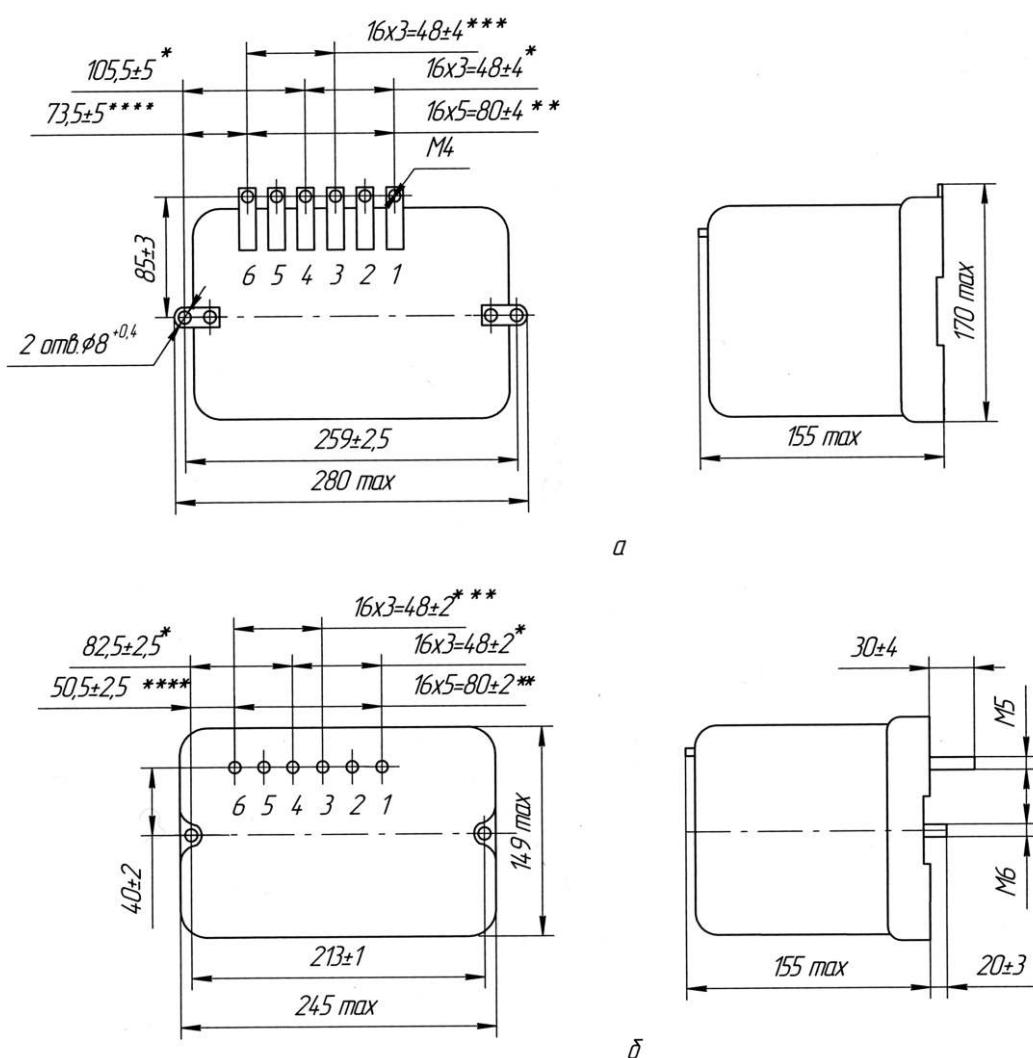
Габаритные, установочные, присоединительные размеры реле серии РТ-80, РТ-90:
